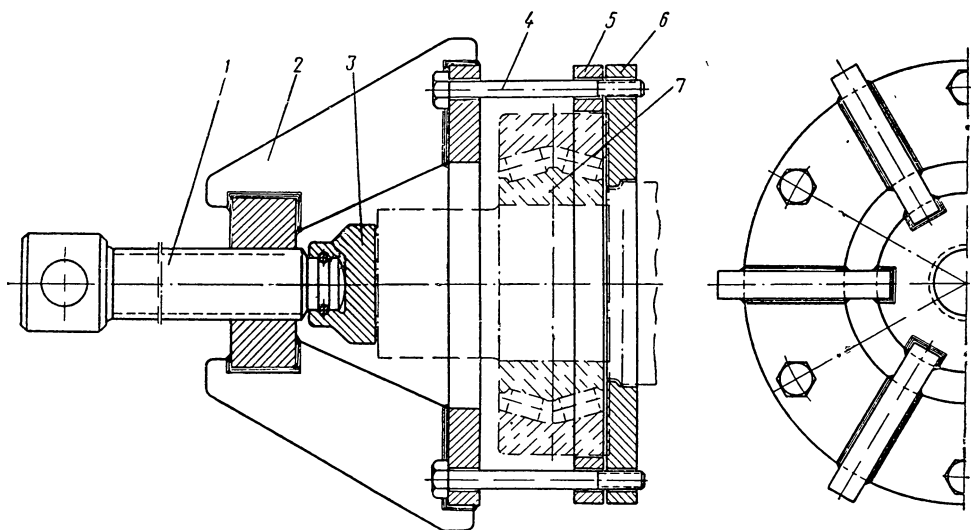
Приспособление для снятия подшипника с вала генератора:
